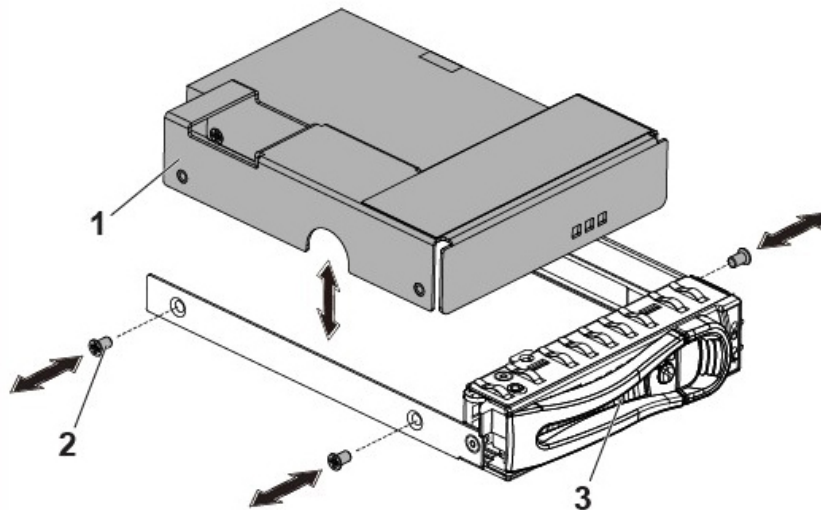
Retrait et installation d'un assemblage d'adaptateur du support de disque dur
